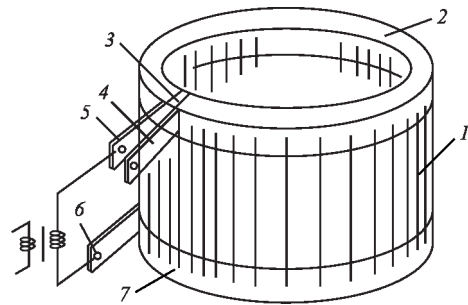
Схема струмопідвідного кристалізатора з електромагнітним обертанням шлакової ванни: 1 — формуюча секція; 2 — струмопровідна секція; 3 — ізолююча прокладка; 4–6 — струмопідводи; 7 — наплавлена заготовка
